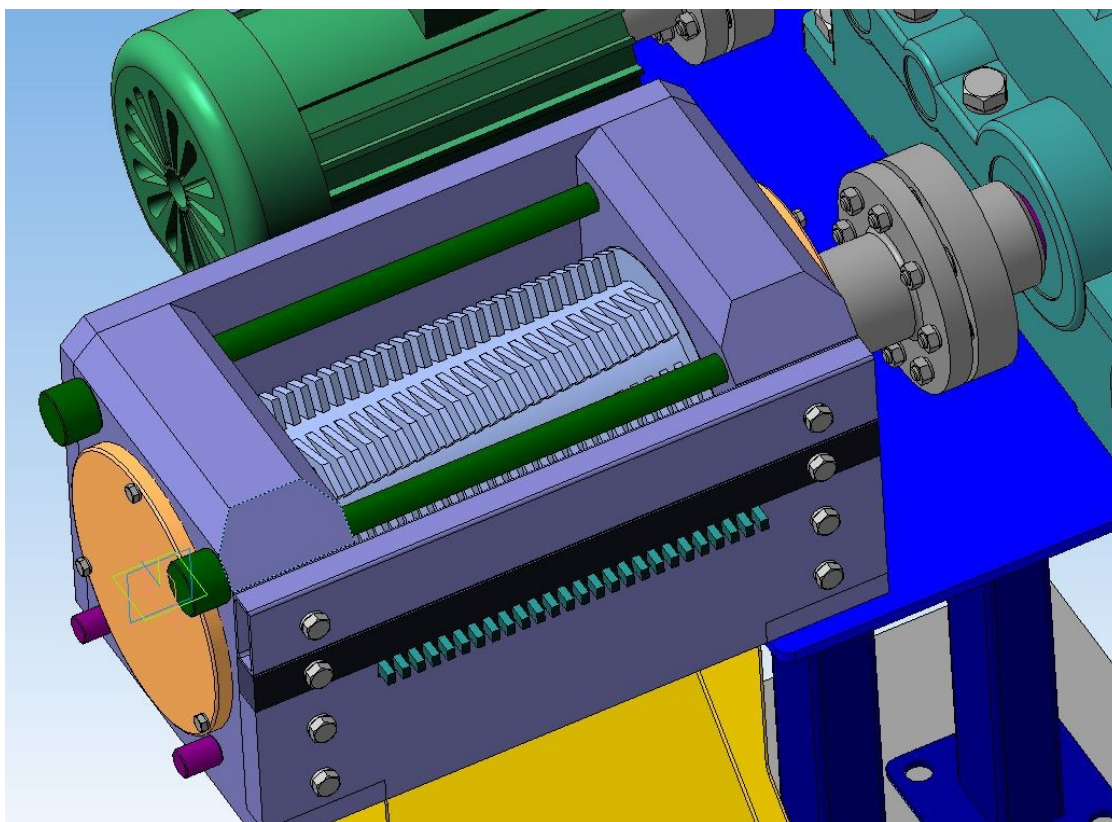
Внешний вид режущего узла одновалкового шредера
